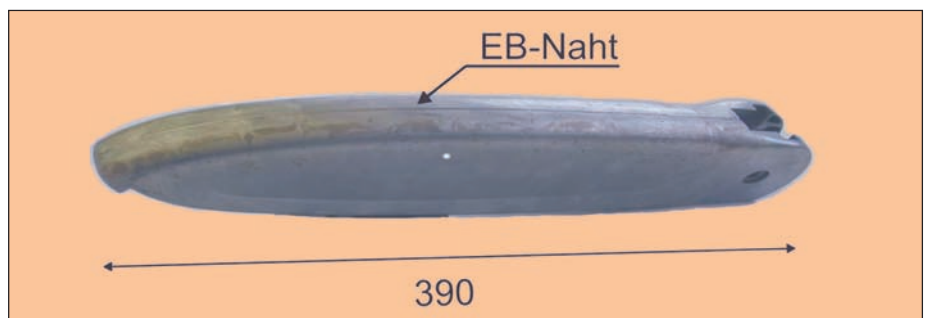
Im Sichtbereich des Elektronenstrahls geschweißtes Bauteil aus Aluminiumdruckguss
